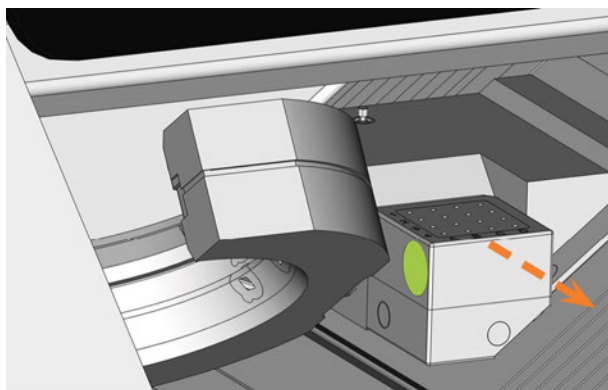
RETIRER LE MAGASIN D'OUTILS (POIGNÉE ENCASTRÉE À GAUCHE EST DE COULEUR VERTE)
